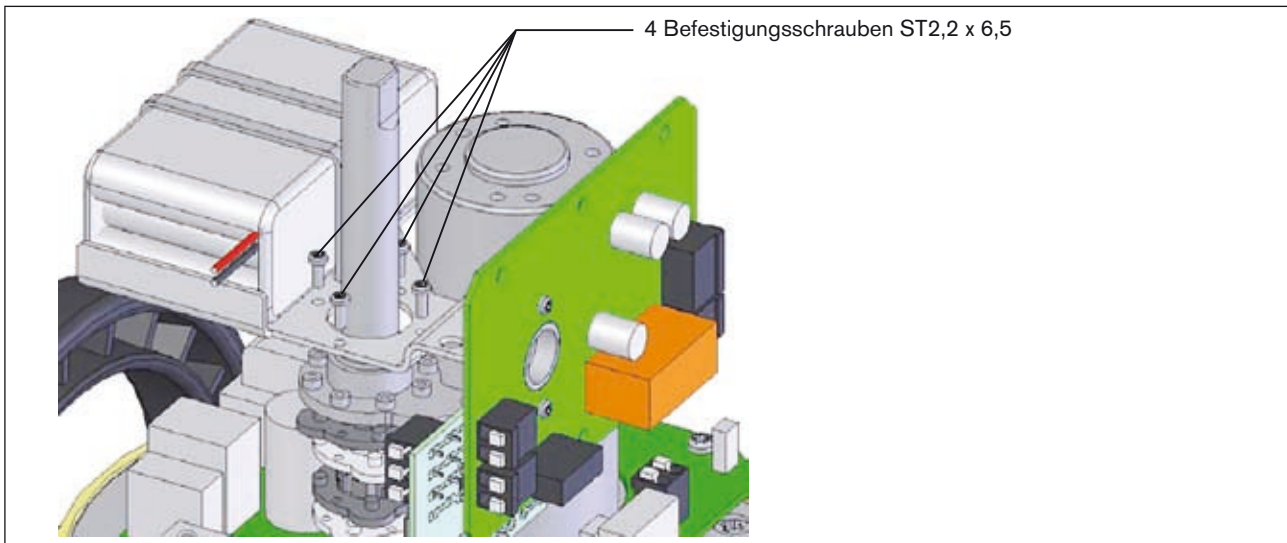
Darstellung: Einbau der Notrückstellung in den Stellantrieb
